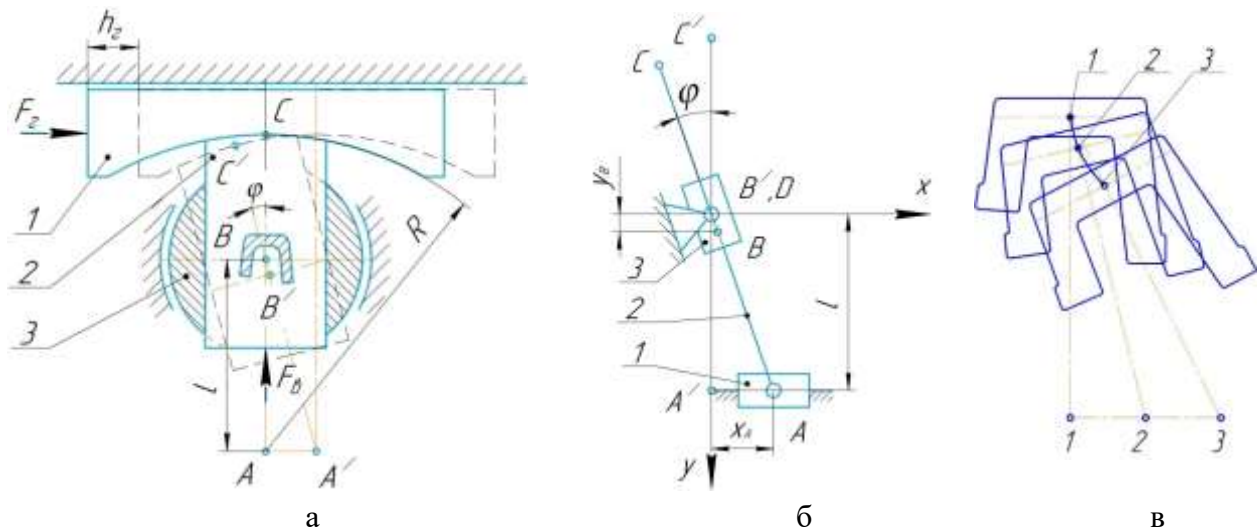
Конструктивна (а), структурна (б) схеми установки клиношарнірного механізму з увігнутим клином із поворотним ножом і траєкторія руху відрізаємої заготовки (в)
